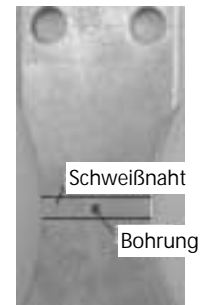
Im Schweißgut gekerbte Dauerschwingprobe aus Magnesium AZ 31 (Nennquerschnitt 20 x 4 mm²)
